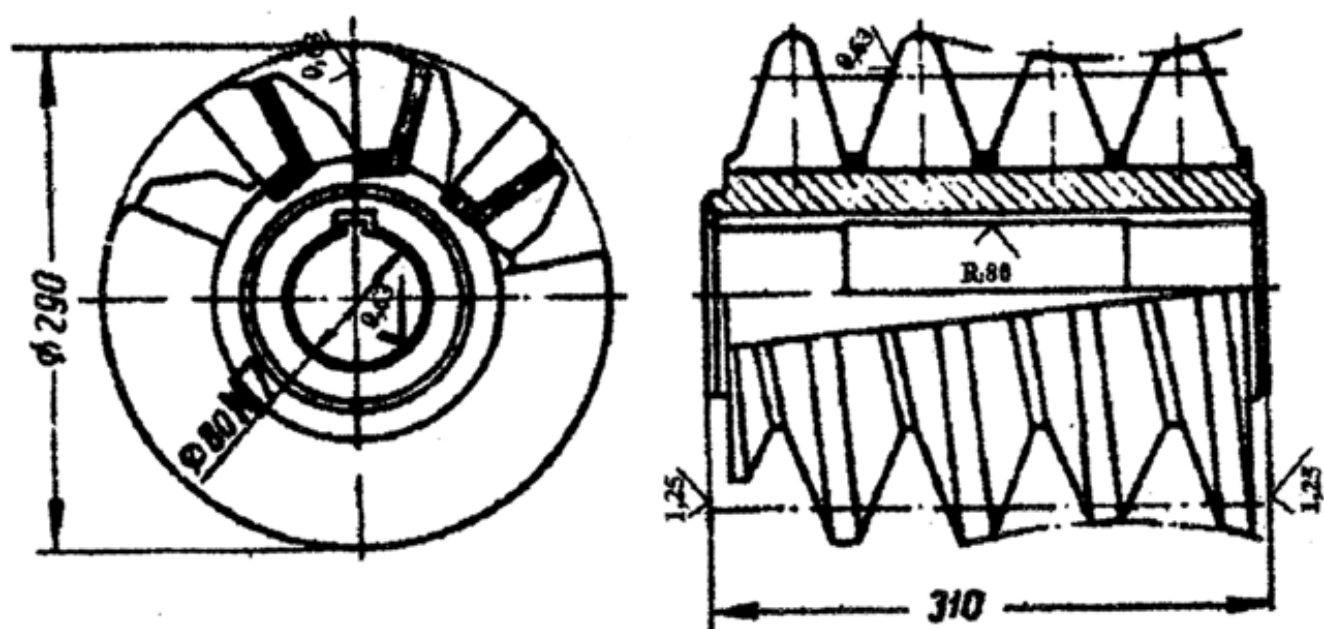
Фреза «Прогресс» сварной конструкции
